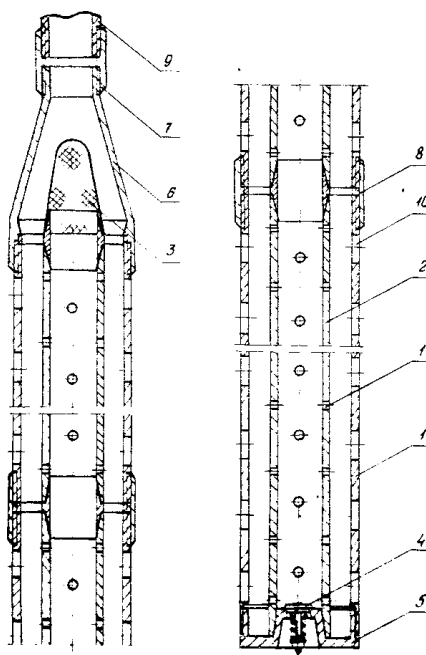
Пристрій для термохімічної обробки свердловин:
